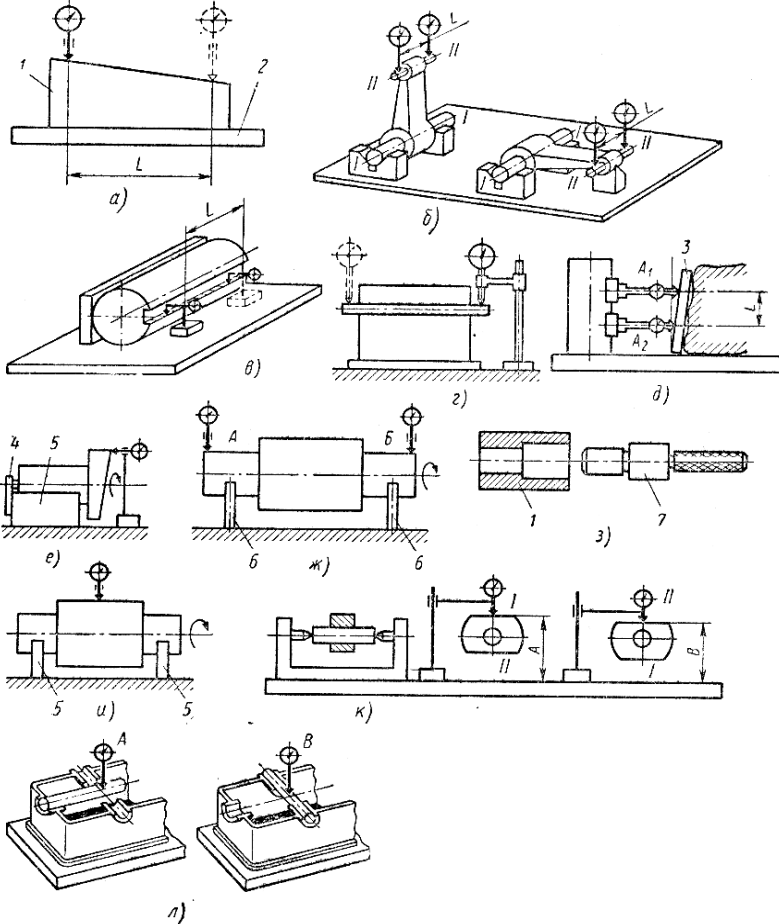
Контроль відхилення розміщення поверхонь: 1 – деталь; 2 – повірочна плита; 3 – призматична підкладка; 4 – упор; 5 – призма; 6 – опора; 7 – калібр.
